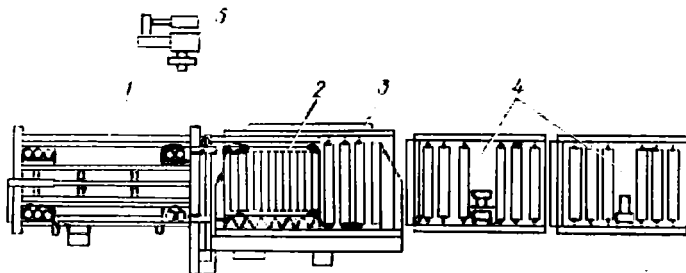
Схема линии сборки коробок дверных блоков ДВ206:
